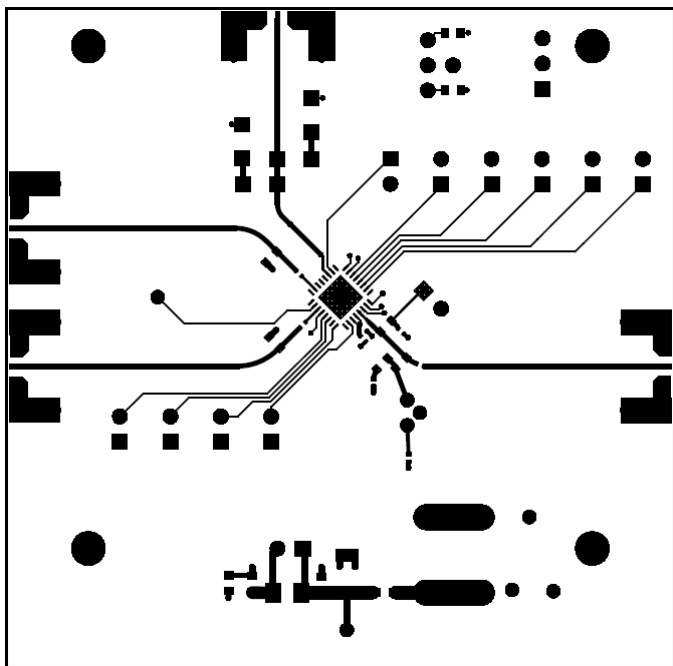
MAX3905 の EV キットの PCB レイアウト—部品面
